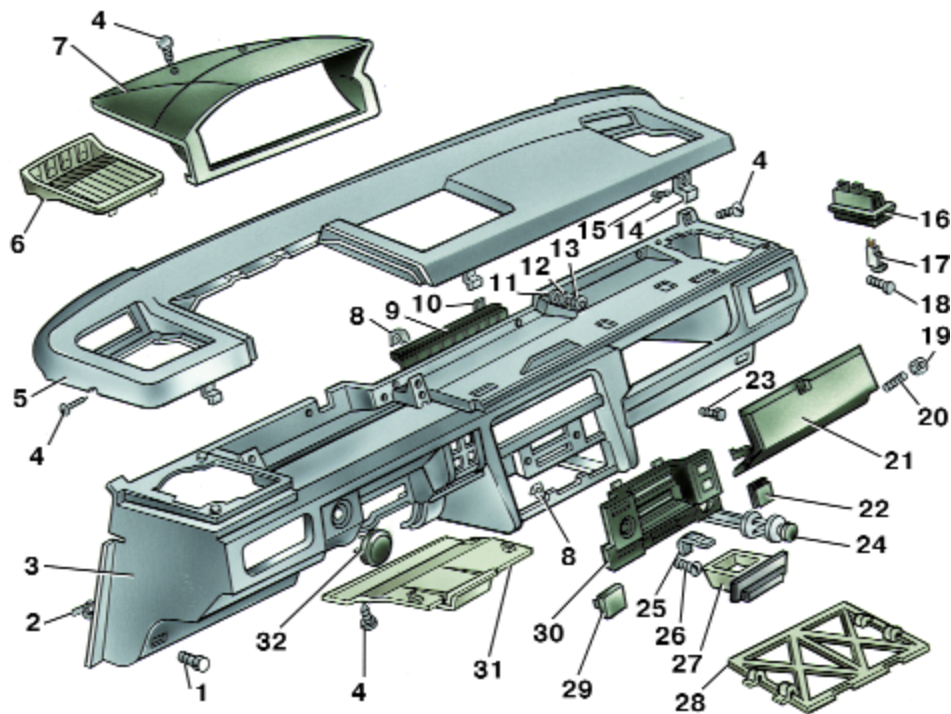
Детали панели приборов: 1 – болт; 2 – гайкодержатель; 3 – панель приборов; 4, 15, 18, 26 – винты; 5 – крышка панели; 6 – решетка панели; 7 – козырек панели; 8 – пластинчатая гайка; 9 – средняя заглушка панели; 10 – держатель; 11 – шайба; 12 – пружинная шайба; 13 – гайка; 14 – защелка крышки; 16 – плафон освещения вещевого ящика; 17 – микровыключатель; 19 – волнистая шайба; 20 – ось петли дверцы; 21 – дверца вещевого ящика; 22 – заглушка гнезда под выключатели; 23 – буфер дверцы; 24 – прикуриватель; 25 – фиксатор пепельницы; 27 – передняя пепельница; 28 – заглушка консоли панели приборов; 29 – заглушка отверстия в накладке под часы; 30 – центральная накладка панели; 31 – заглушка люка панели; 32 – боковая заглушка панели
